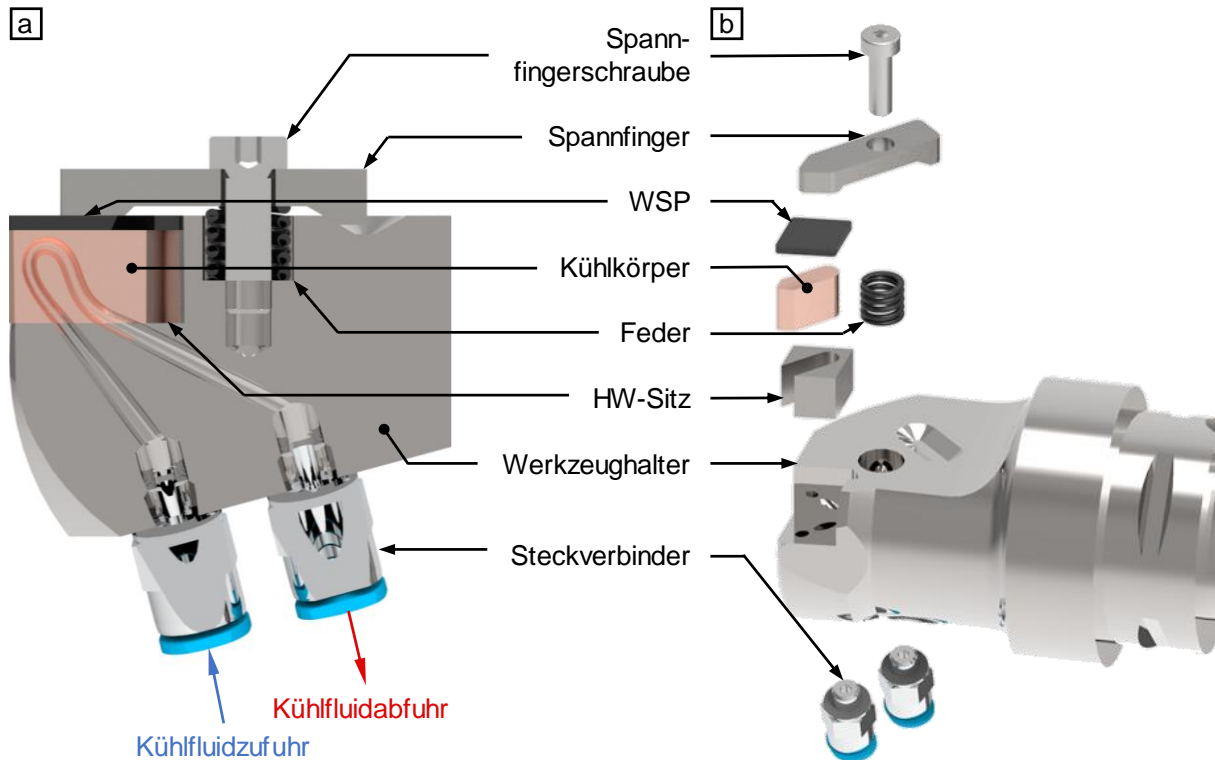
Zweiter Vorentwurf; a) Schnittansicht; b) Explosionsansicht
